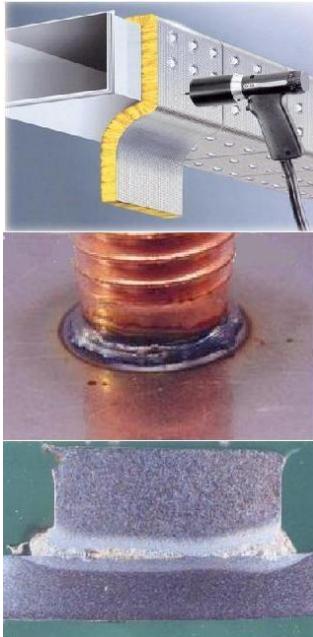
Примеры использования рассмотренных технологий сварки крепежных деталей.
